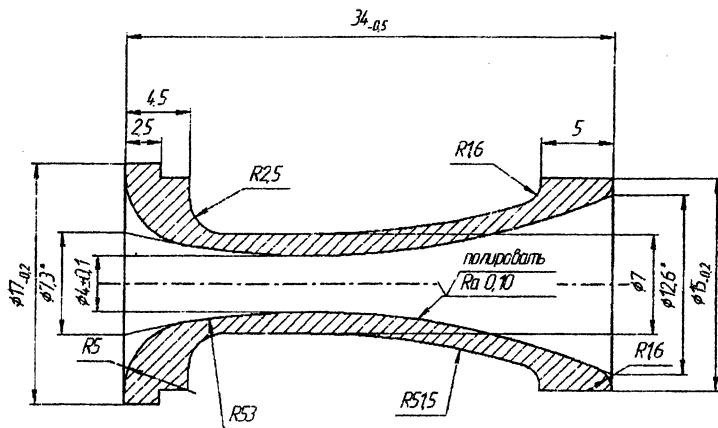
Эскиз детали «Проводка таза машин RI-10, RIR-15»
